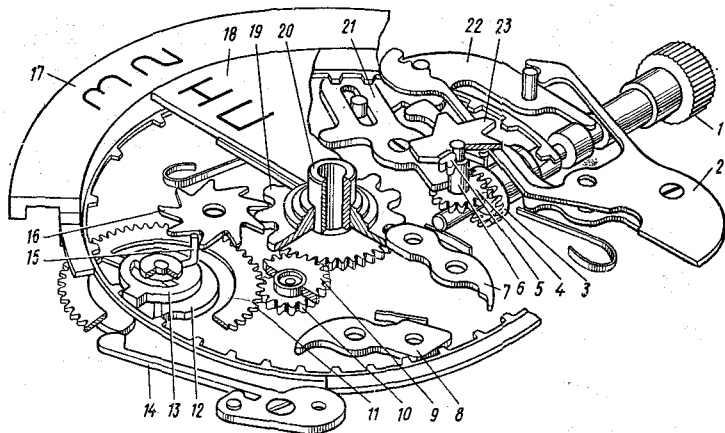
Кинематическая схема календарного устройства кварцевых часов с шаговым двигателем 3050:
